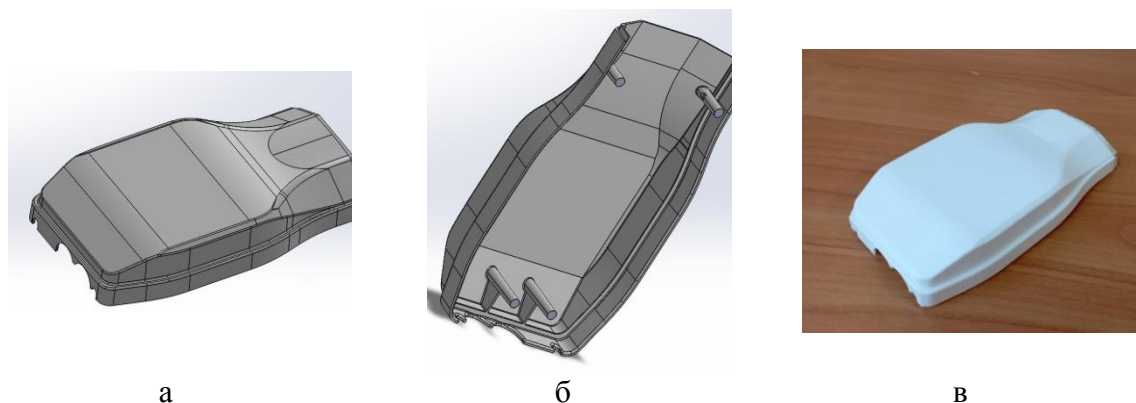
Верхний кожух: 3D модель (а,б) и изготовленная деталь (в).
